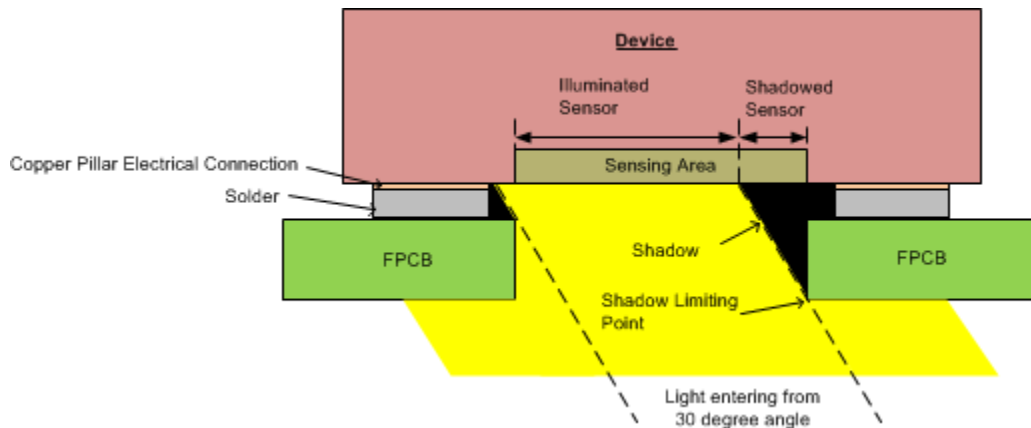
PicoStar™ 器件（焊接到带切口的 FPCB 上，光从某个角度进入）横截面图
